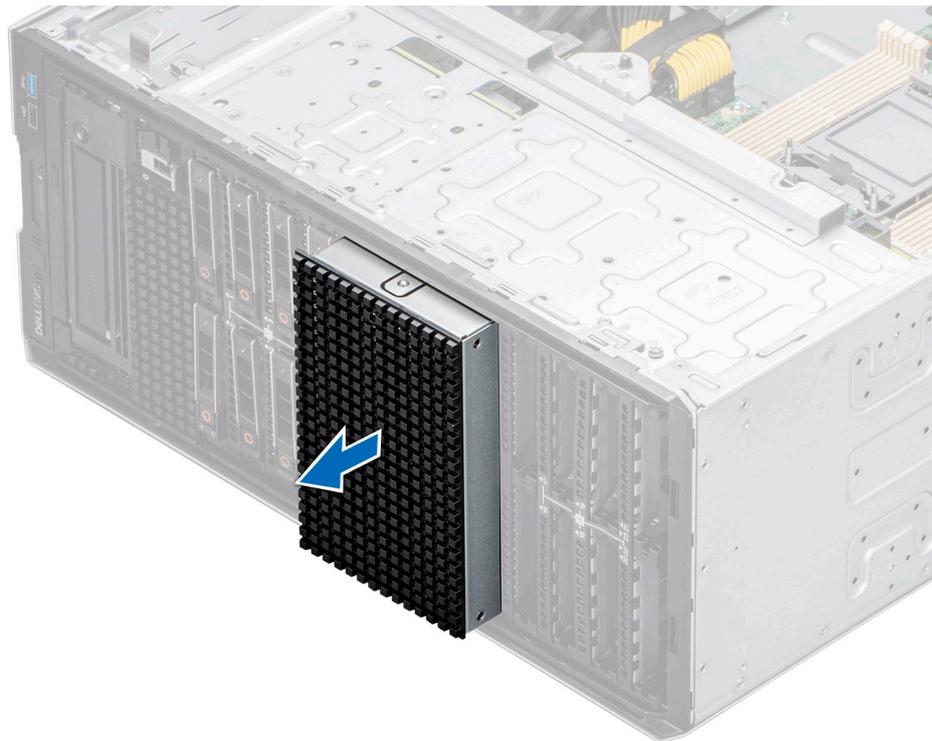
Entfernen des Platzhalters für das Laufwerkschachtgehäuse
